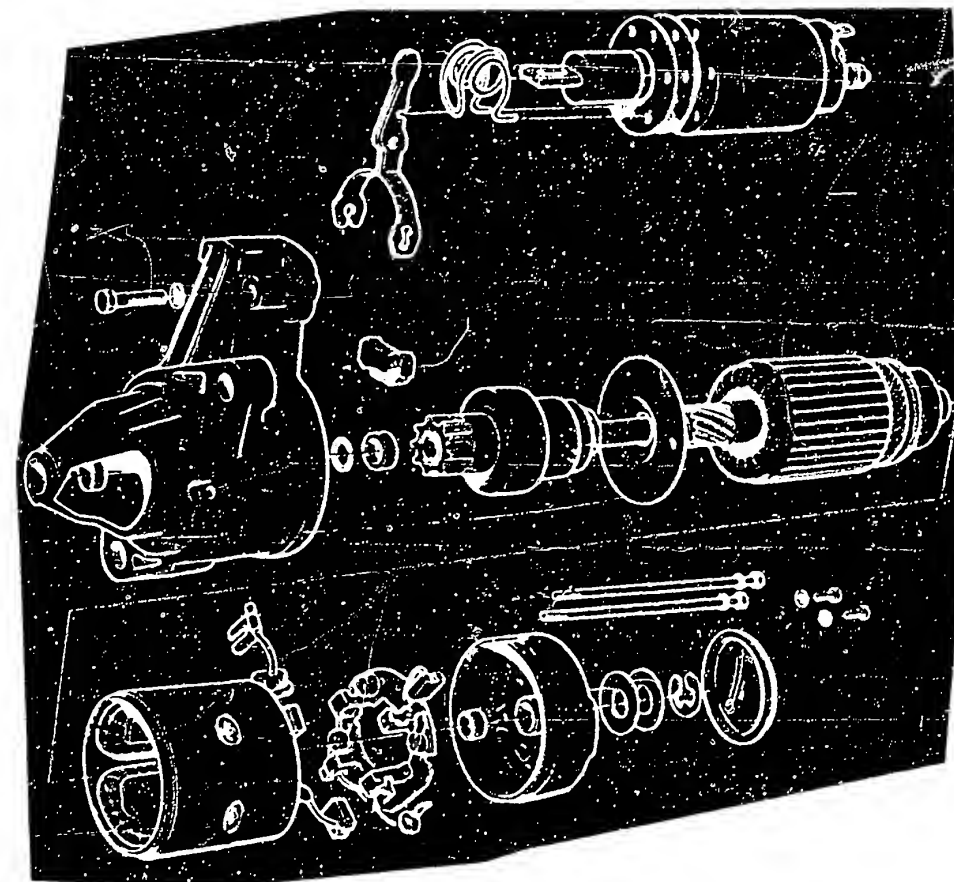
Der Hitachi- Anlasser S114-232 in seine Einzelteile zerlegt.
